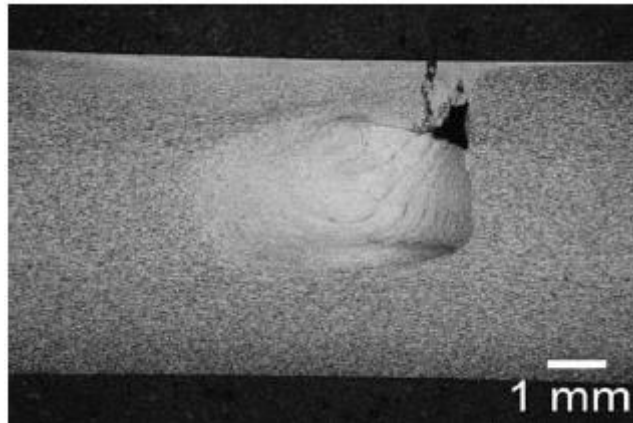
Macrografia mostrando vazio em uma solda por *Friction Stir Welding*.
